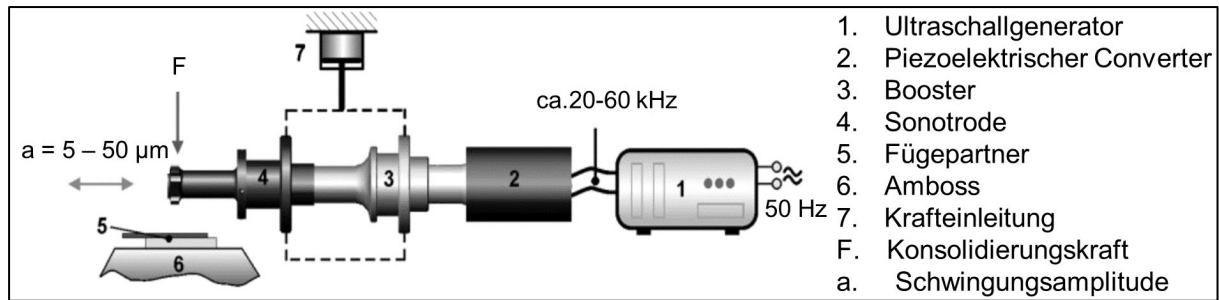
Typischer Aufbau einer Ultraschallpunktschweißanlage für Metallschweißungen aus [63]
